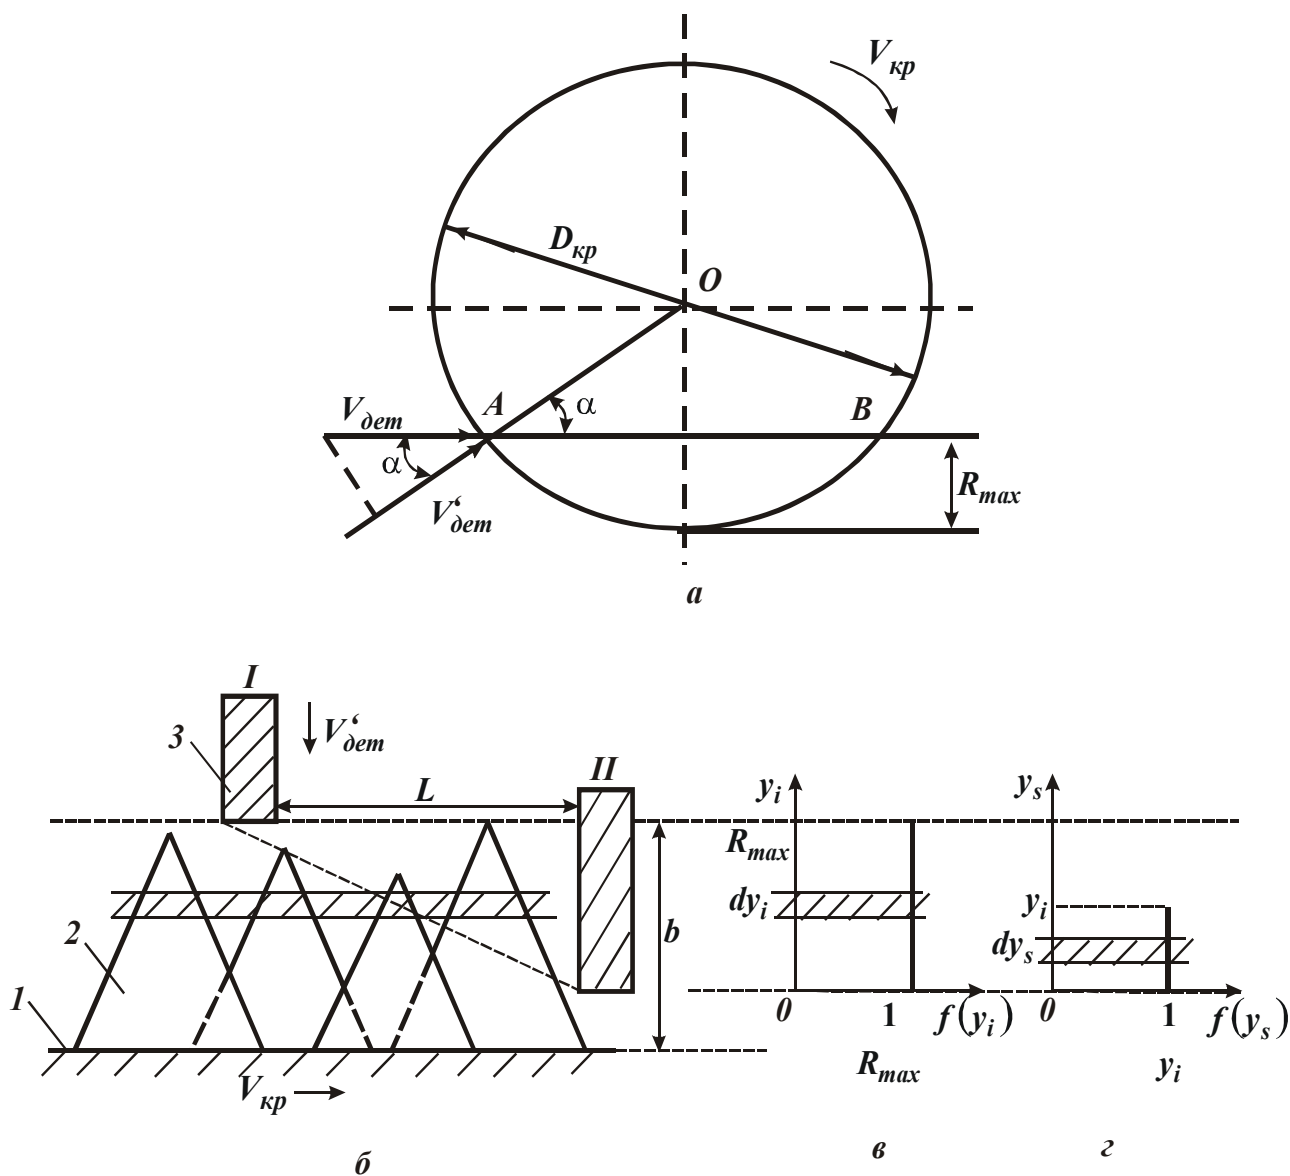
Расчетная схема шероховатости поверхности: 1 – уровень связки круга; 2 – режущее зерно; 3 – обрабатываемый образец.
